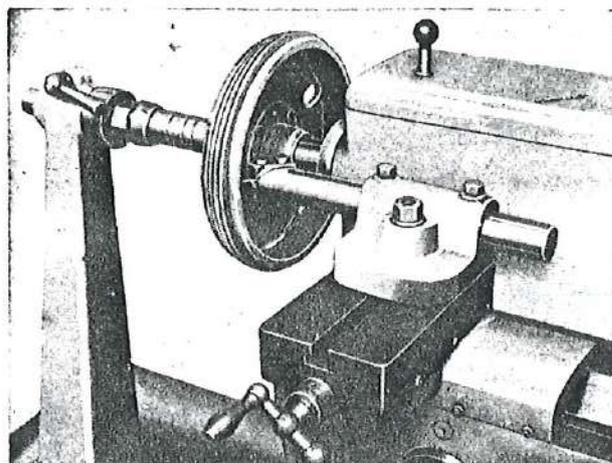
Torneado de un tambor de frenos sobre el torno M. 10.
